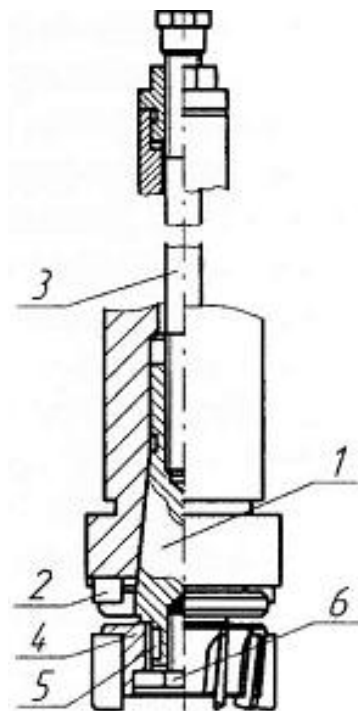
Схема закріплення фрези на оправці зі шпонкою
